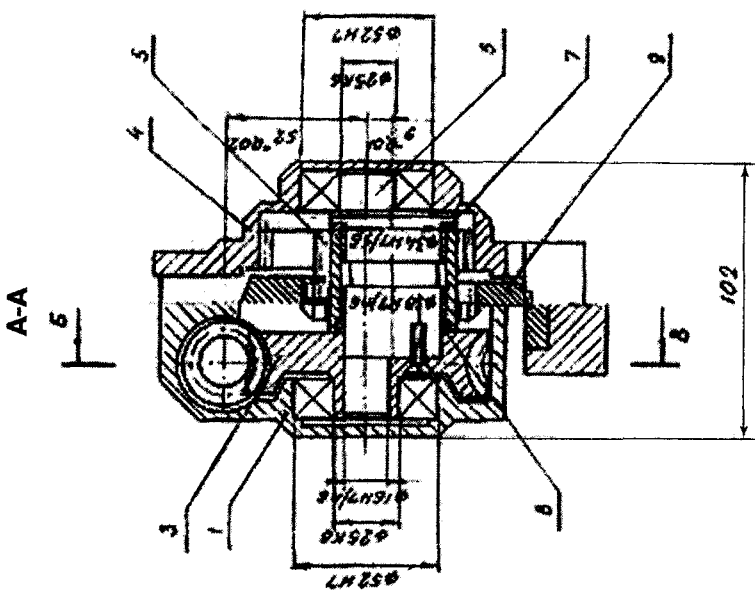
Общий вид насадки: 1 – корпус; 2 – червяк; 3 – колесо червячное; 4 – колесо центральное; 5 – сателлит; 6 – вал эксцентриков; 7, 8 – втулки; 9 – нож подвижный; 10 – тело ножа; 11 – пластина противорезущая; 12 – прокладка
